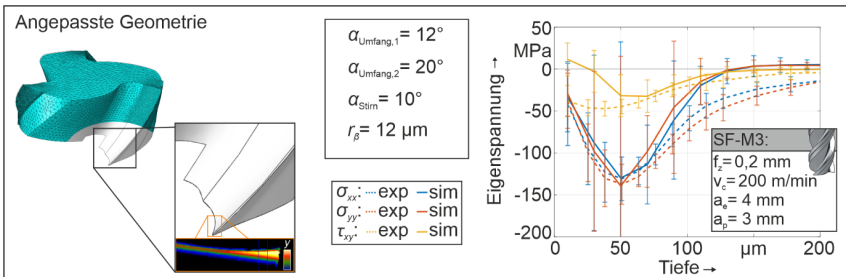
Vergleich simulierte und gemessene P-ES für angepasste Werkzeuggeometrie (SF-M3)
